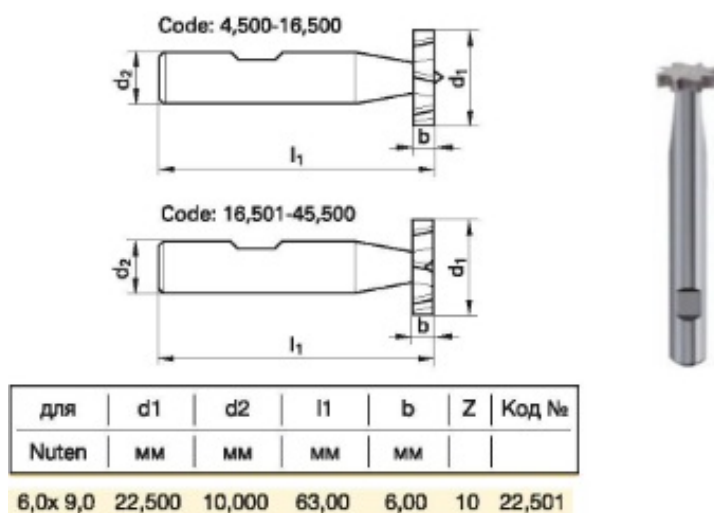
Быстрорежущая грибковая фреза Guhring 850 (3580).
